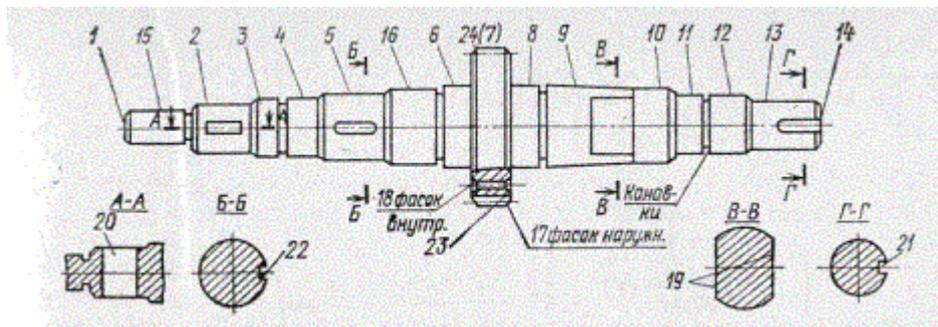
Пример типовой избыточной детали с разметкой поверхностей (элементов) обработки
